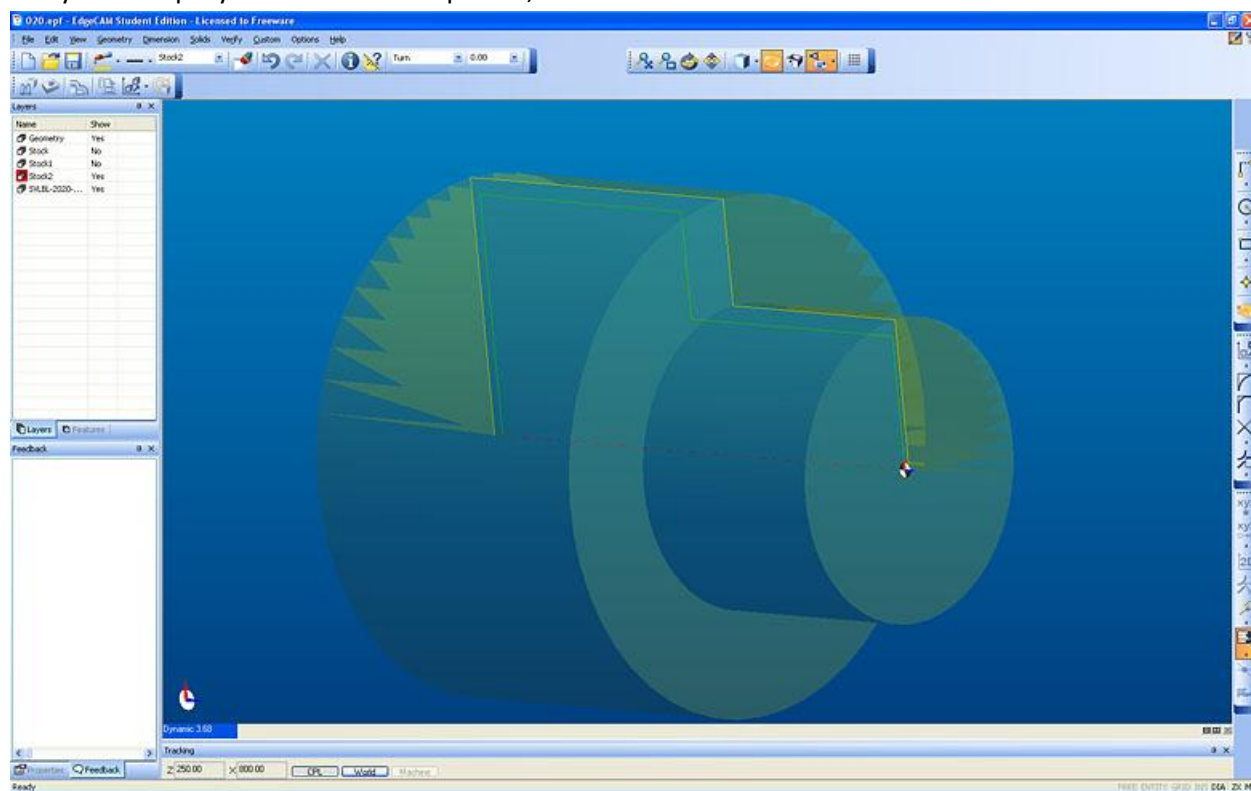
Edgecam. Создание заготовки для токарной обработки
